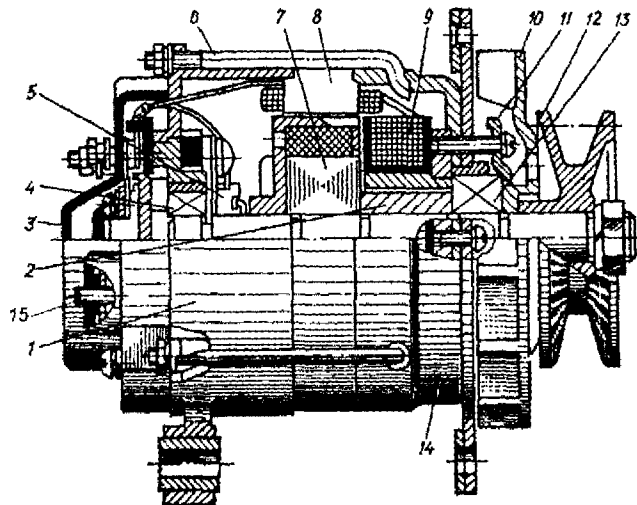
Генератор 46.3701: 1 - задняя крышка; 2 - втулка ротора; 3 - крышка регулирующего устройства; 4 - выпрямитель; 5 - стяжной болт; 7 - ротор; 8 - статор; 9 - катушка возбуждения; 10 - вентилятор; 11 - крышка подшипника; 12 - шкив; 13 - подшипник; 14 - передняя крышка; 15 - винт переключателя сезонной регулировки напряжения
